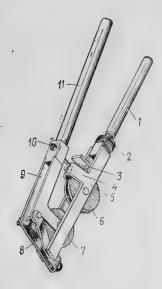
1— рычаг нижний; 2— ролик; 3— ролик обжимной; 4—крючок; 5—рычаг верхний; 6— ручка пластмассовая
